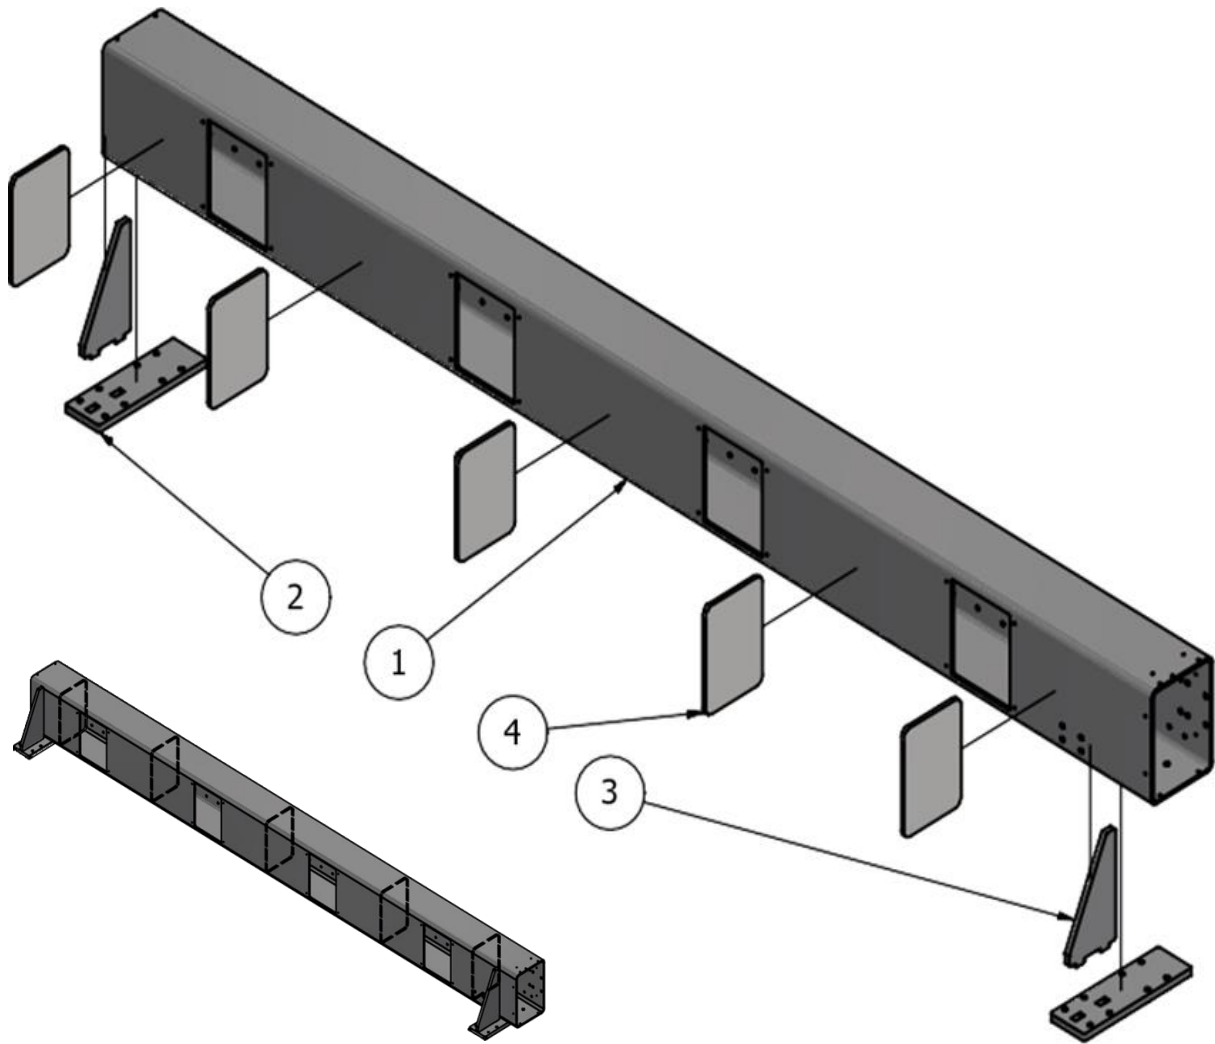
Estrutura soldada da base M&G_PMM_F_H:
